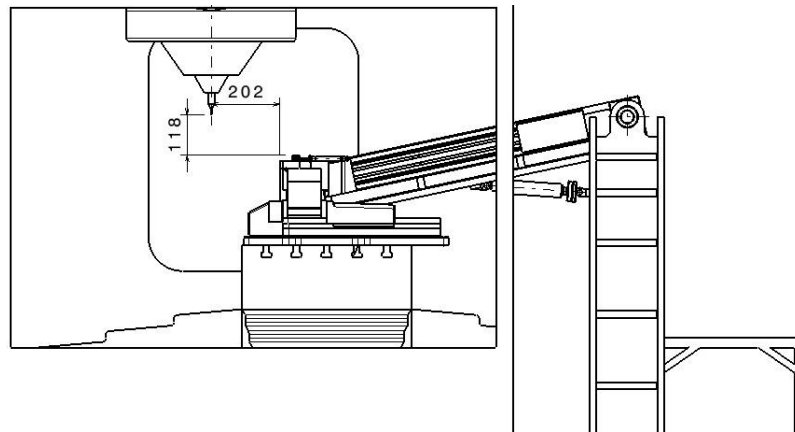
Dimensão de segurança entre a porta do centro de usinagem e o alimentador
